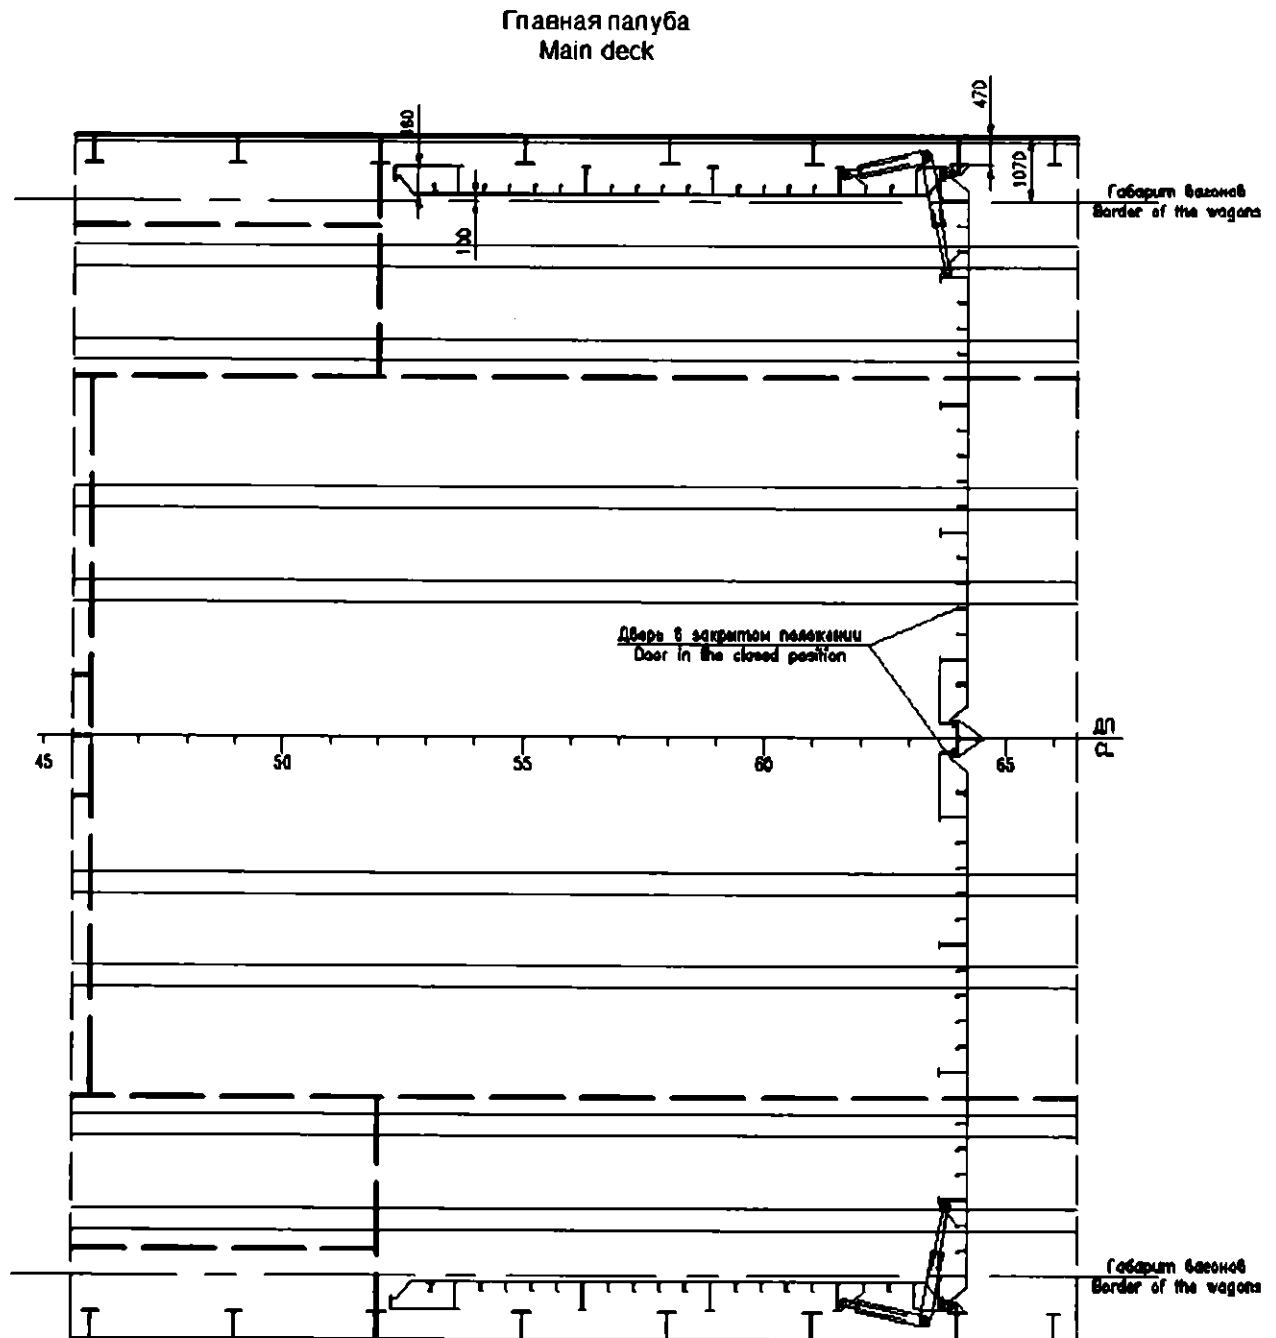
Габаритные размеры вид сверху / Overall dimensions top view.
